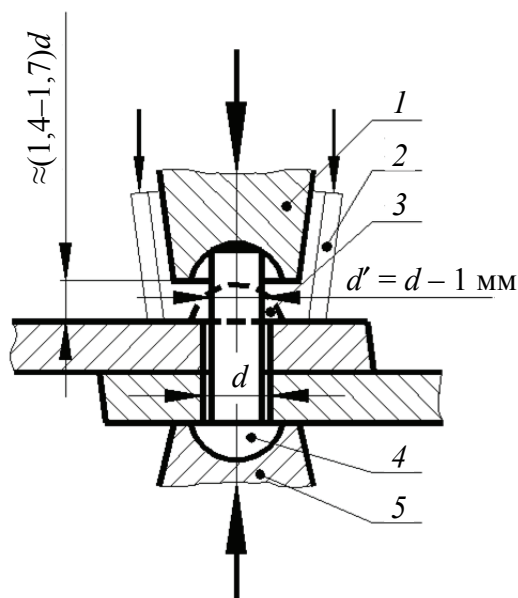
Схема процесса клепки заклепочного соединения:
